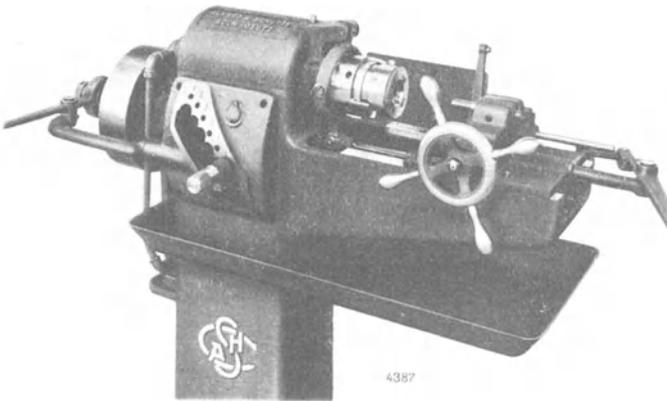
Schraubenschneidmaschine. A. H. Schütte, Köln.
